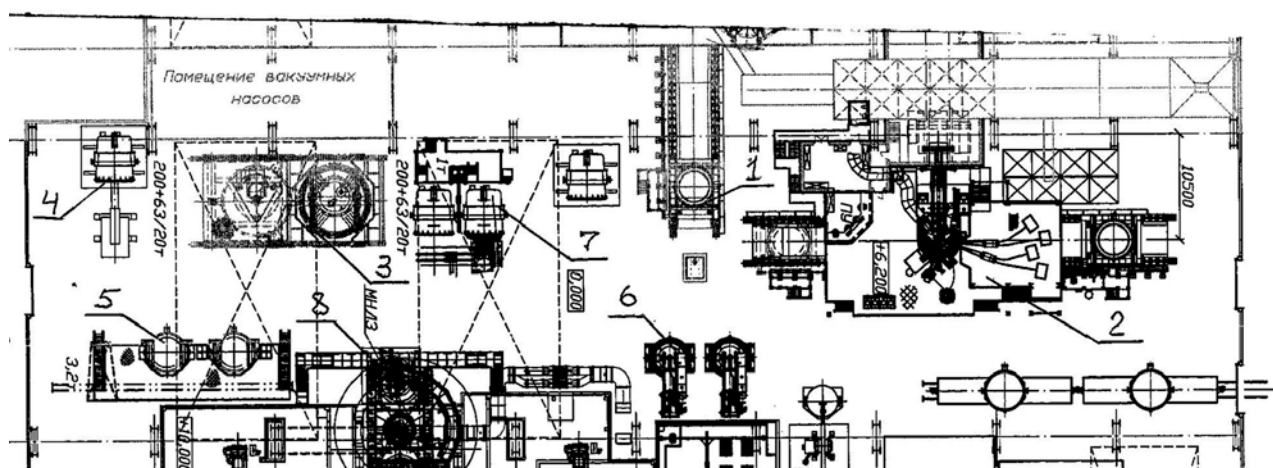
План ковшевого пролета ЭСПЦ: 1 — стелевоз с ковшом; 2 — установка ковш-печь; 3 — установка вакуумирования стали; 4 — ломка футеровки сталеразливочных ковшей; 5 — место для кладки новой футеровки сталеразливочных ковшей; 6 — стенды для сушки футеровки; 7 — стенды для нагрева футеровки сталеразливочных ковшей; 8 — поворотный стенд МНЛЗ
